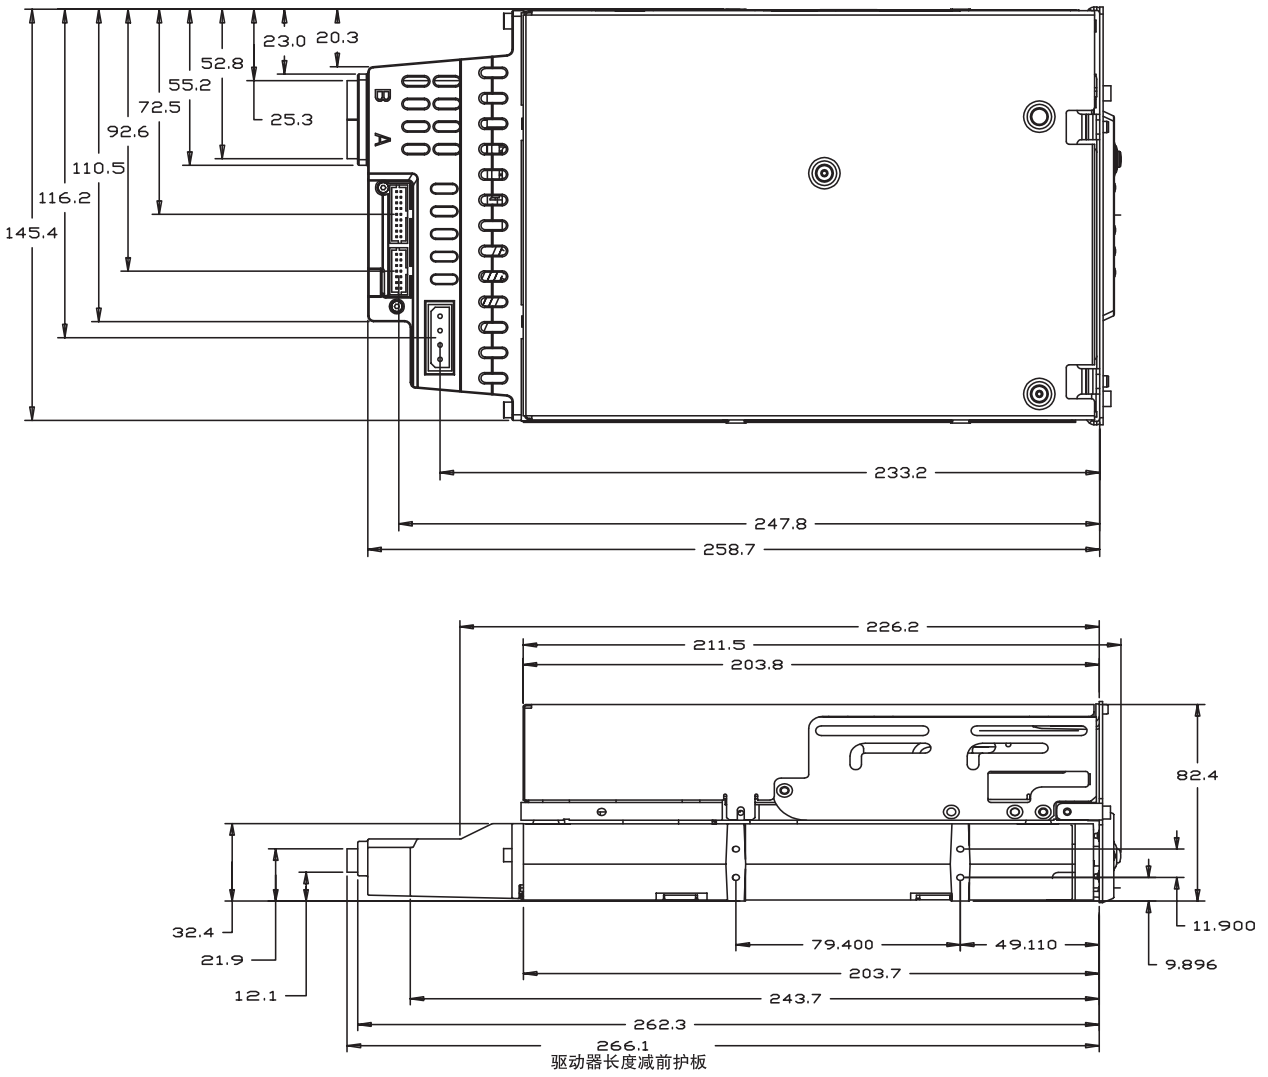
光纤通道内部 Viper 驱动器 — 尺寸
